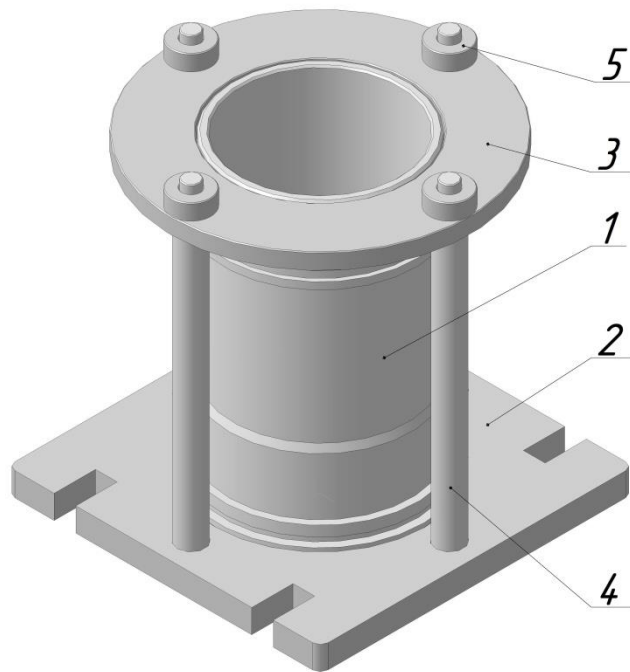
Збірне установочне пристосування для обробки робочої порожнини гільзи циліндра ДВЗ
